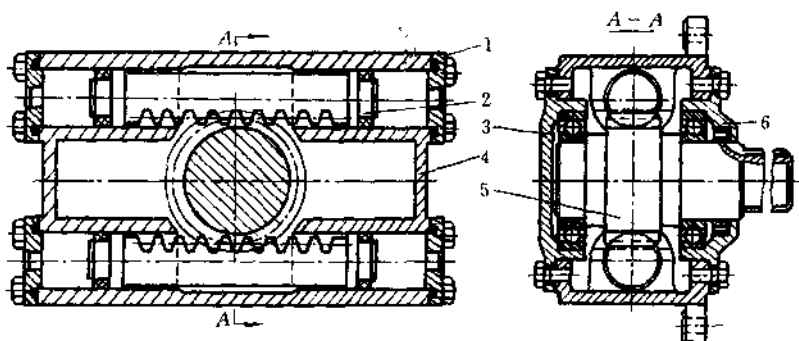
双缸式齿条齿轮式摆动液压缸
